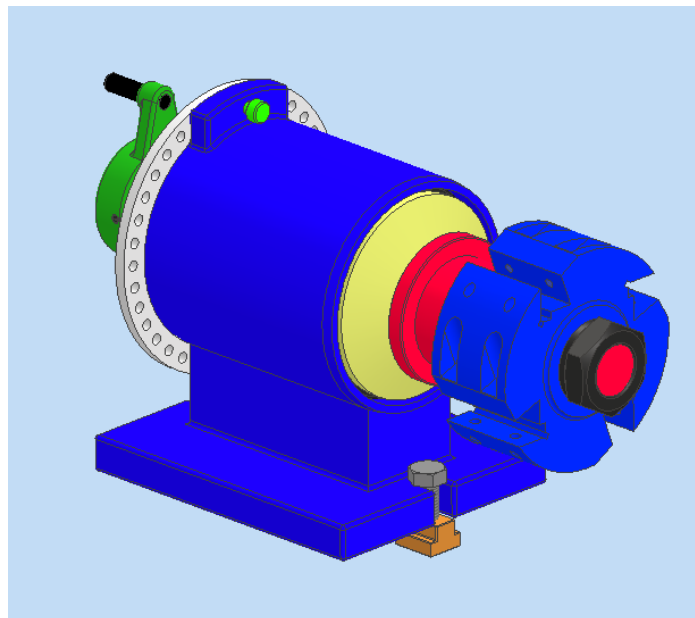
Пристосування для фрезерування пазів із закріпленою фрезою
